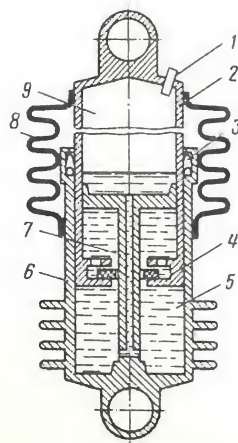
Устройство узла подвески: 1 — клапан для накачки воздуха; 2 — стальной верхний цилиндр; 3 — уплотнительные манжеты; 4 — клапан амортизатора; 5 — амортизационная жидкость; 6 — дюралюминиевый нижний цилиндр с охлаждающими ребрами; 7 — шток с поршнем; 8 — резиновая защитная гармошка; 9 — верхняя полость со сжатым воздухом.
